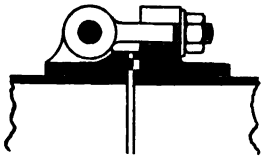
Flanschverbindung mit Scharnierbolzen.
